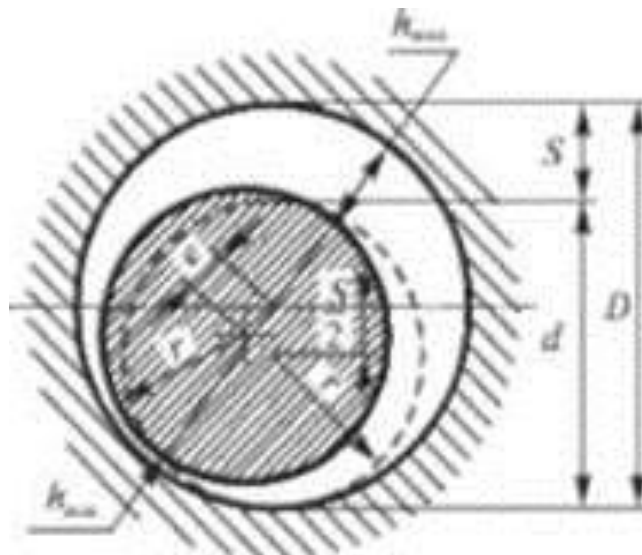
Схема до розрахунку посадок з зазором в підшипниках ковзання
